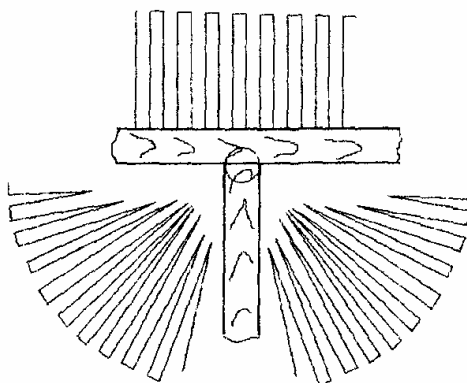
Схема контроля зоны пересечения сварных соединений
